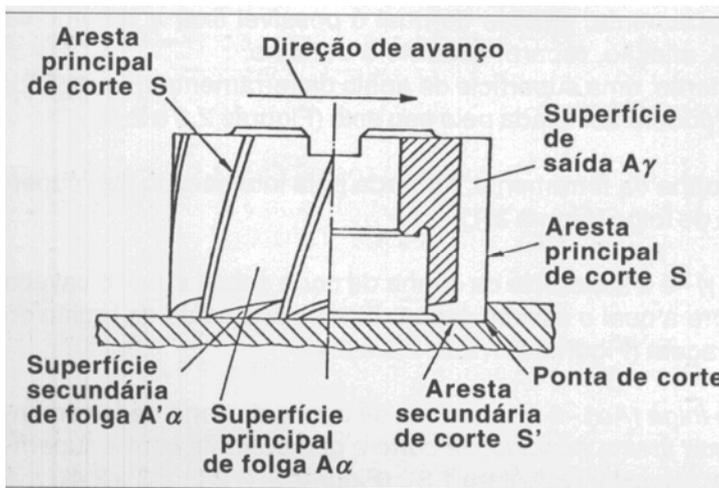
Aresta de corte e superfícies da parte de corte de uma fresa frontal
